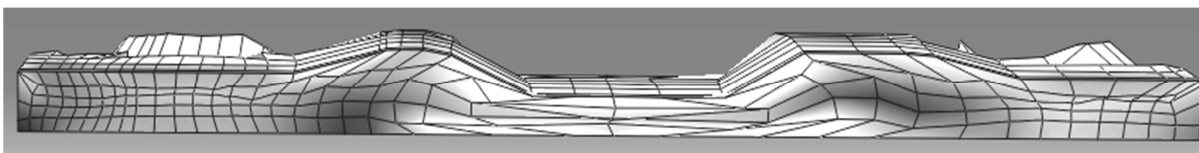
Результати моделювання пластичного деформування заготовки деталі «U-імплантат» з різними розмірами
